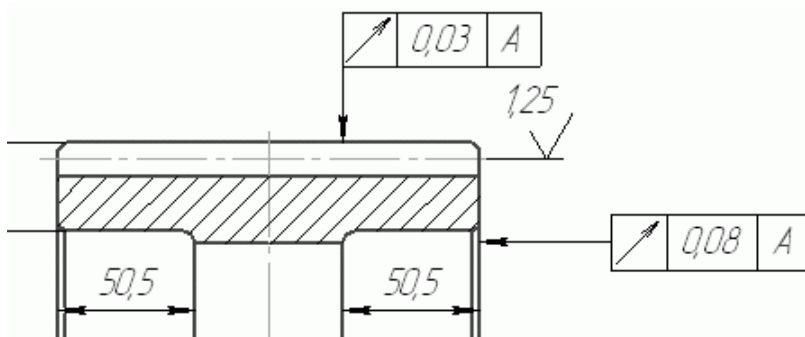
Допуски формы и размещения поверхностей
